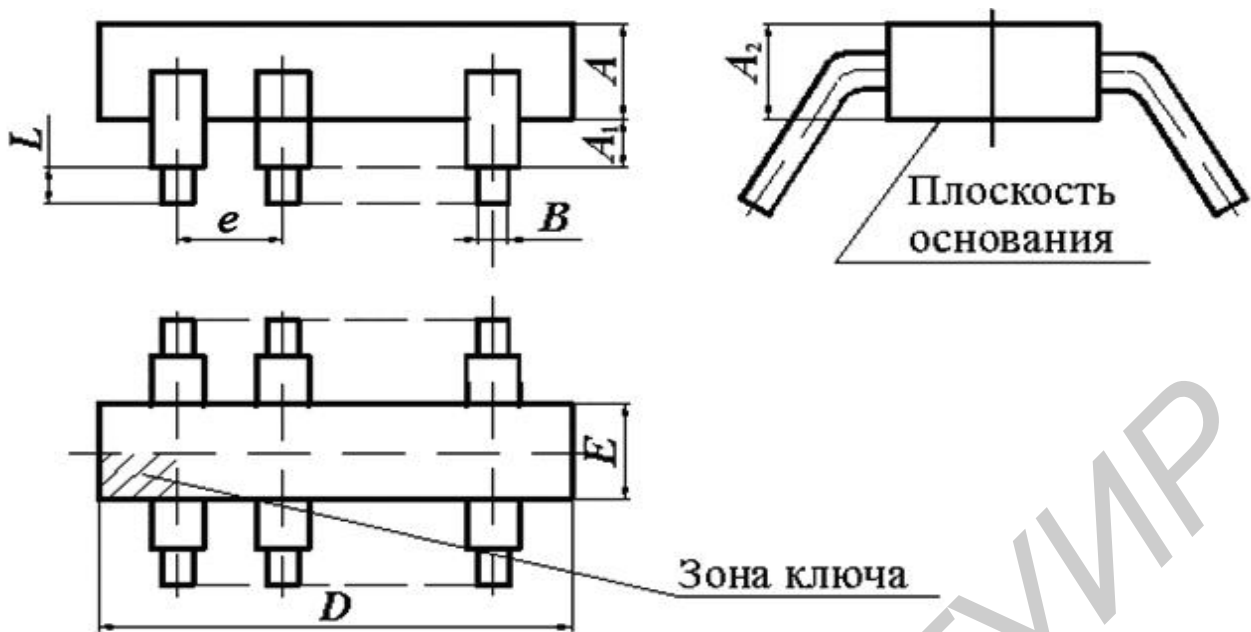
Обозначение размеров ИМС в корпусах типа 2
